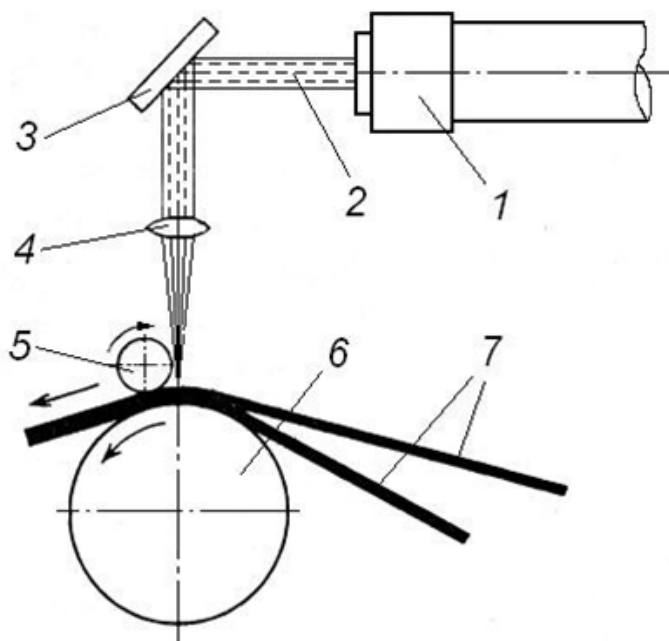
Схема зварювання плівок лазерним випромінюванням: 1 – лазер; 2 – промінь; 3 – дзеркало; 4 – фокусуюча лінза; 5, 6 – ролики; 7 – зварювальні плівки.
